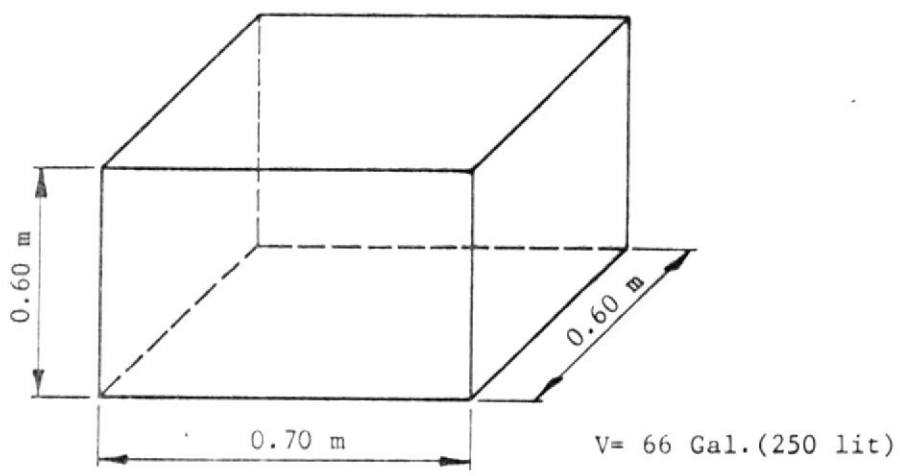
DIMENSIONES FINALES DEL TANQUE DE ACEITE
